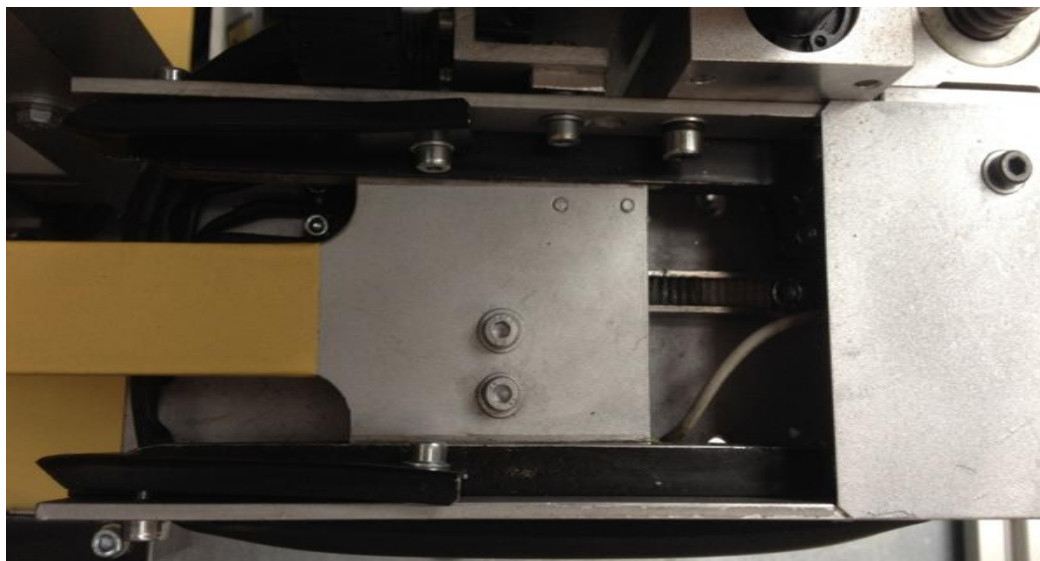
Nové řešení pohybu zakladače palet v ose y
